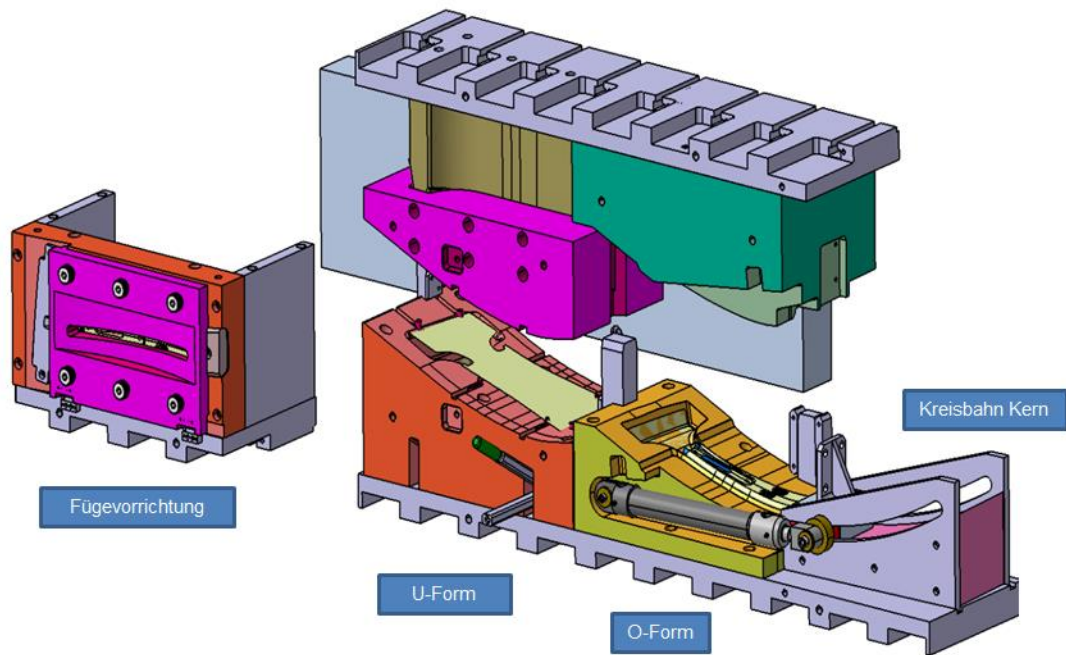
Layout des T³-Formgebungswerkzeugs
